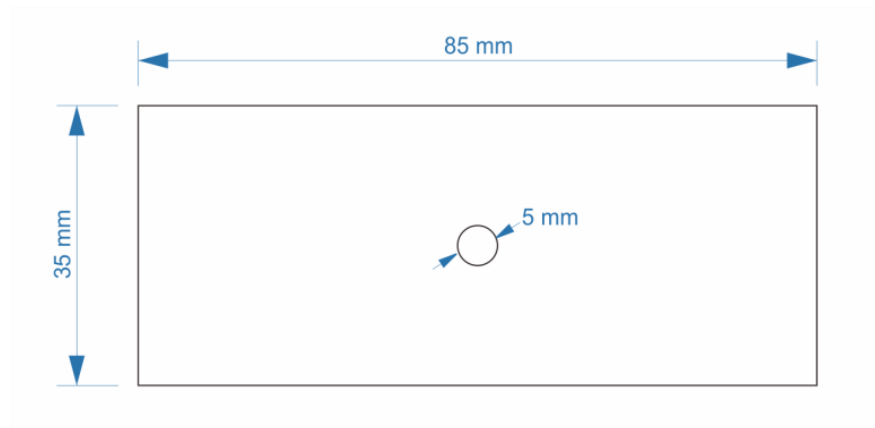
Dimensi ukuran benda kerja plat aluminium 1100.
